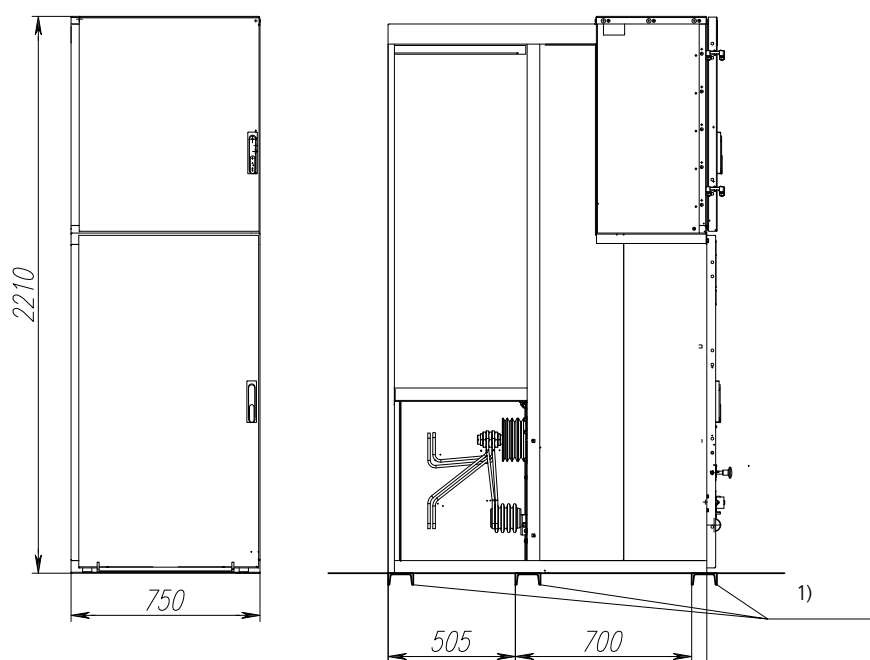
Общий вид и габаритные размеры шкафа К-128 с измерительными ТН на номинальные токи до 1600 А
